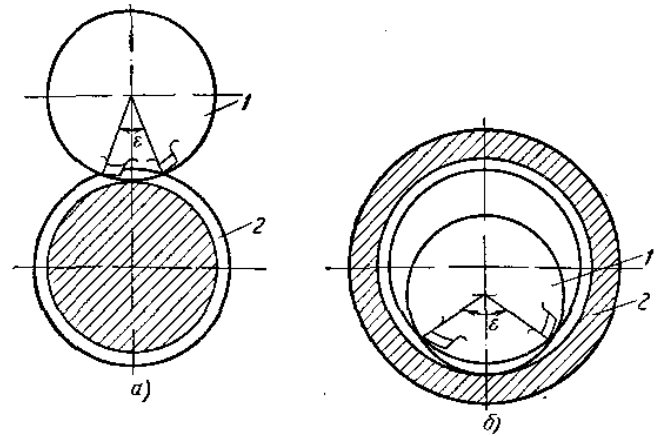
Угол контакта и дуга контакта фрезы с обрабатываемой заготовкой:
